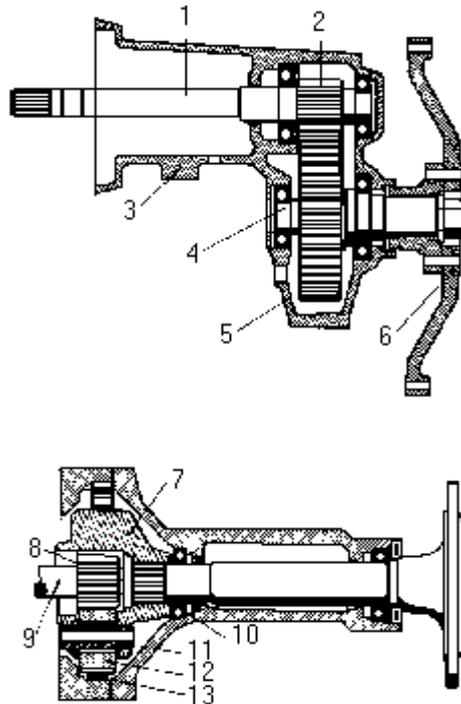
Representação de um redutor final de carretos com dentes diretos colocado junto à roda.
